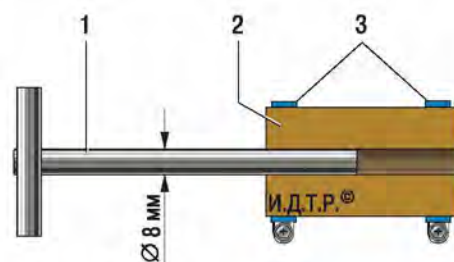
Приспособление для притирки клапанов: 1 – металлический стержень; 2 – резиновый шланг; 3 – винтовые хомуты
